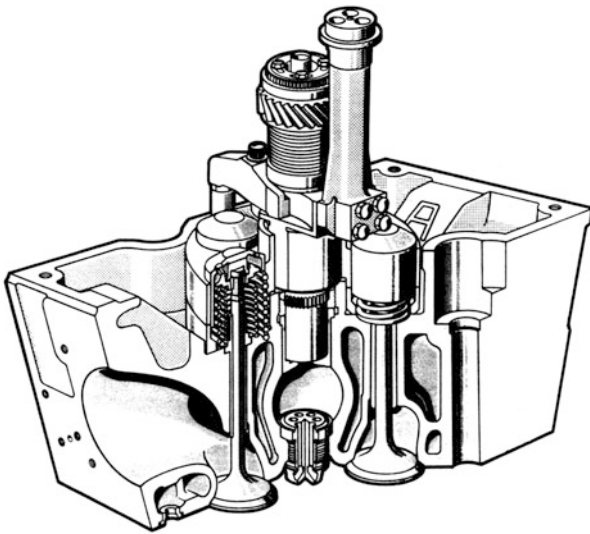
Zylinderkopf mit Vorkammer, Brenner, Einspritzgerät (Pumpedüse) und sechs Ventilen
